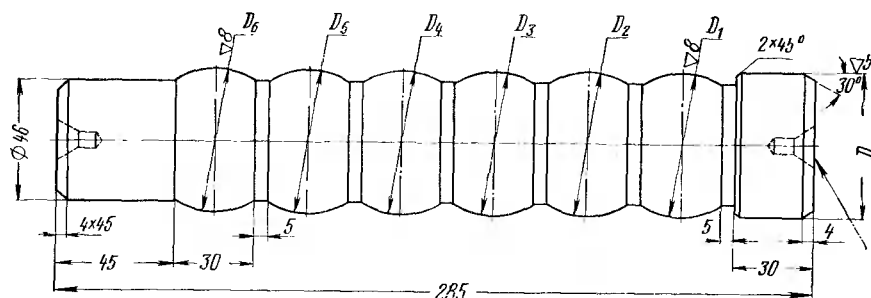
Прошивка для раздачи шейки под подшипник дифференциала
